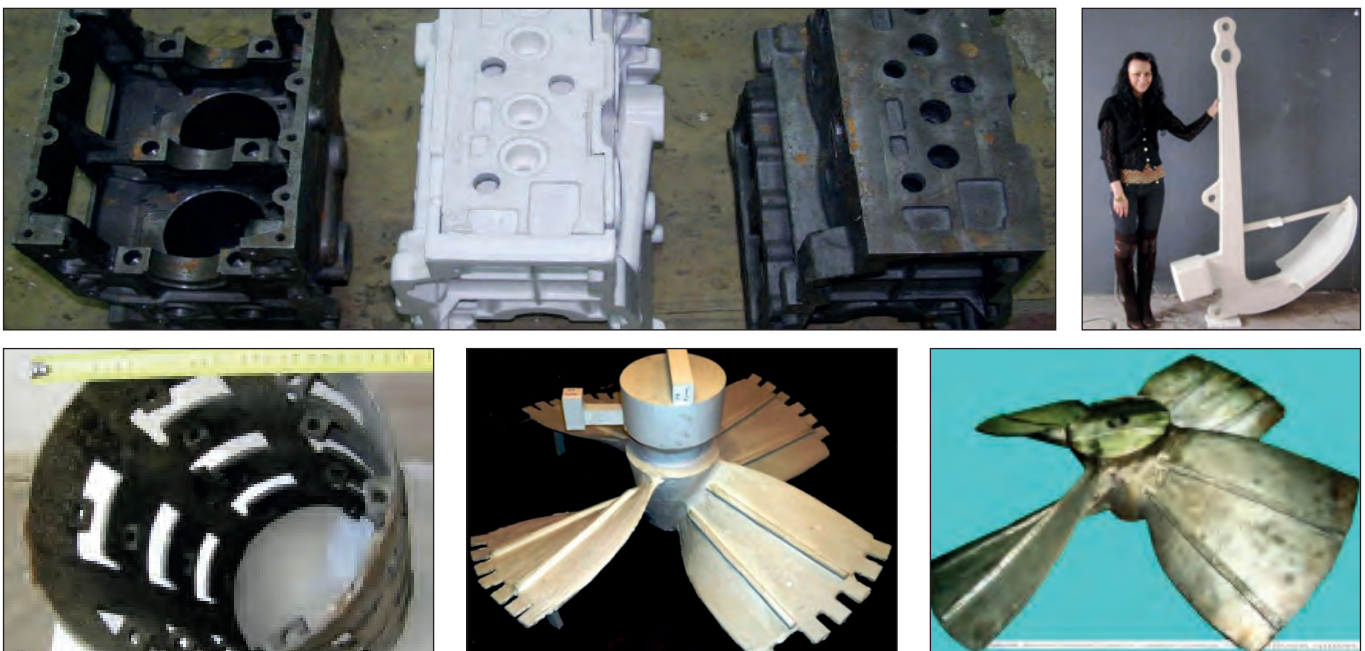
Виливок і модель 2-циліндрового двигуна (ДВЗ) для електрогенератора бронемашини; модель якоря корабля; корпус касетної корзини для боеприпасів; модель гребного гвинта і його виливок із нержавіючої сталі
